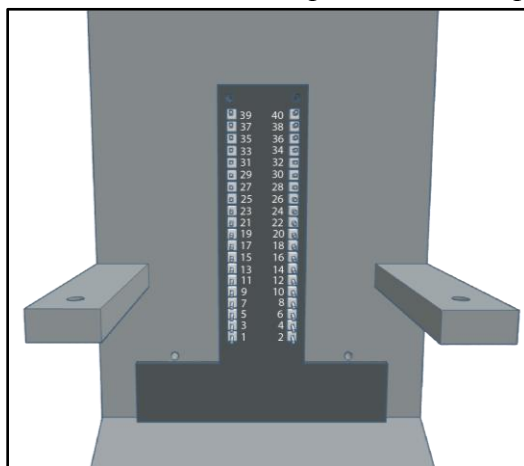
Установка GPIO адаптера РетнаБокс.
